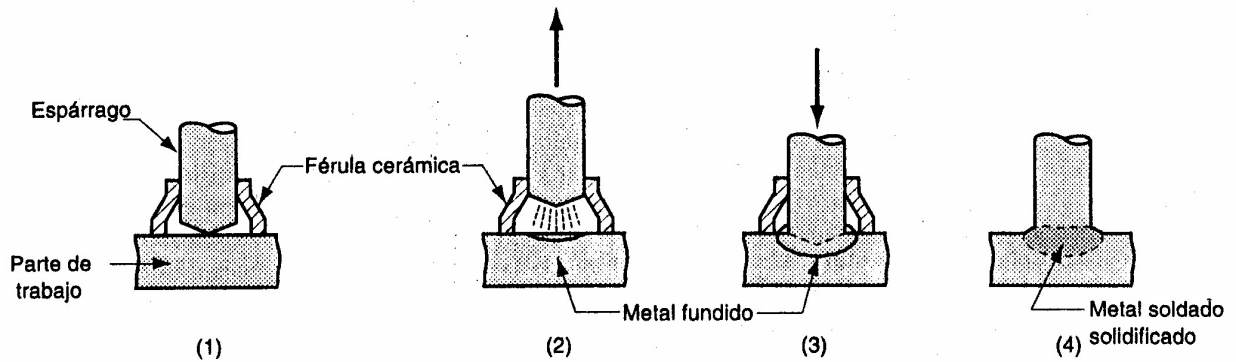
Soldadura de espárrago SW: (1) Se coloca el espárrago o perno; (2) Fluye la corriente desde la pistola y se jala el espárrago desde la base para establecer un arco eléctrico y crear un pozo fundido; (3) Se hunde el espárrago en el pozo fundido; (4) Se remueve la férula cerámica tras la solidificación.
